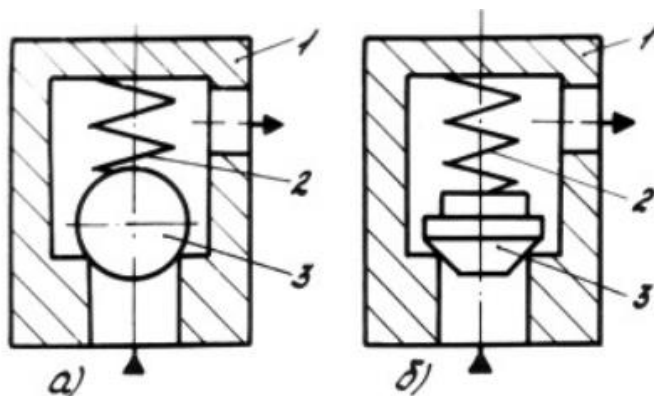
Схема обратных гидравлических клапанов: а) шарикового типа: 1 – корпус; 2 – пружина; 3 – шарик; б) конусного типа: 1 – корпус; 2 – пружина; 3 – конус.
